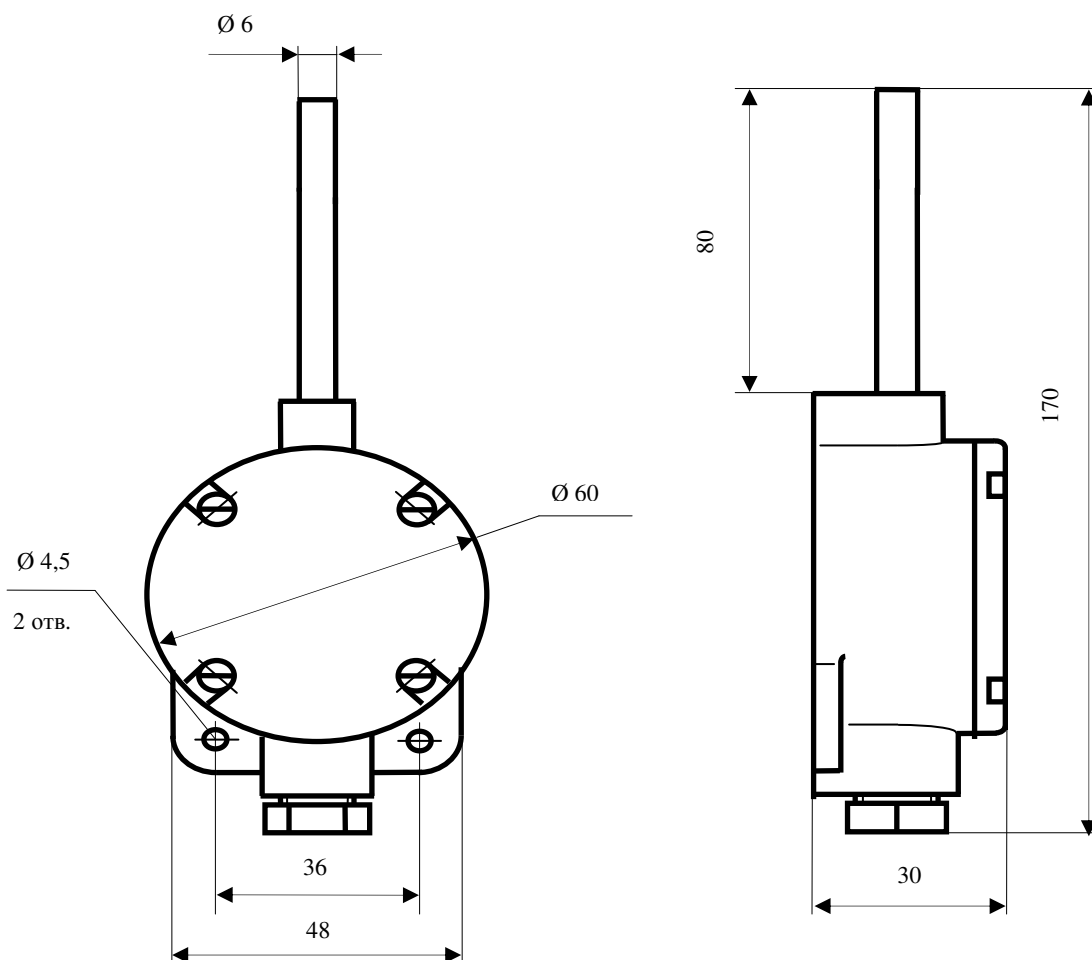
Термопреобразователь TSM 0618-04. Габаритные и присоединительные размеры.
